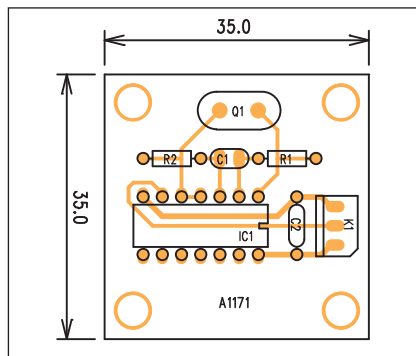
Rozložení součástek na desce druhého oscilátoru
